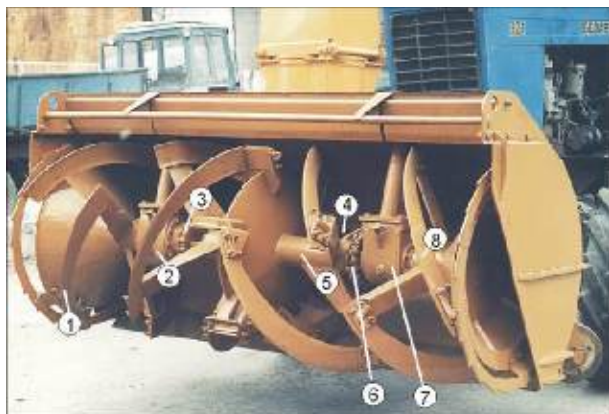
Снегопогрузчик: 1 – корпус; 2 – питатель; 3 – ножи зачистные; 4 – опорный ролик; 5 – щека; 6 – рассекатель; 7 – редуктор раздаточный; 8 – редуктор кожуха; 9 – кожух раздаточный.
